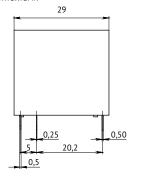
Габаритные, установочные, присоединительные размеры pene OptiRel G RP40-52 и OptiRel G RP40-61 с CO контактами
